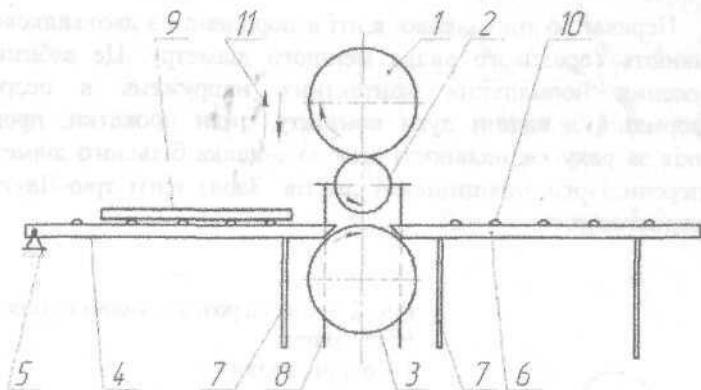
Схема тривалкового стану Лаута: 1, 3 – приводні валки великого діаметру; 2 – середній холостий валок; 4 – підйомно-коливальний стіл; 5 – опора; 6 – паралельно-підйомний стіл; 7 – штанги підйому столів; 8 – штанга підйому і опускання середнього валка; 9 – розкат; 10 – ролики; 11 – напрям переміщення верхнього валка для зміни зазора між валками
